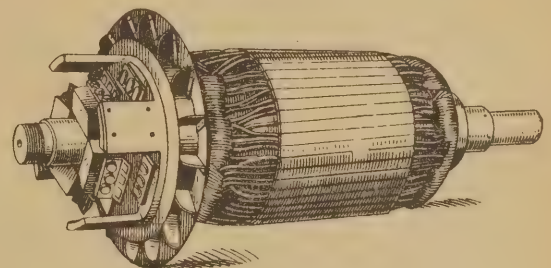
Rotor eines Weißberg-Simplex-Motors mit Fliehkraftschalter.
